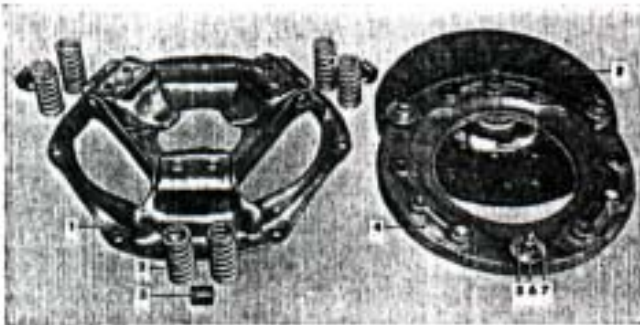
Embrague "AUBURN" (mod. 130274).
